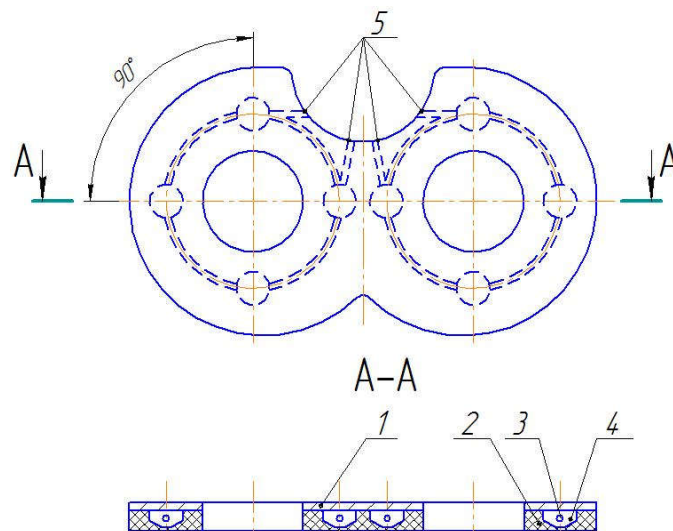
Конструкція пластини компенсації торцевого зазору: 1 - робоча поверхня; 2 - опорна поверхня; 3 - пружнодемпфуючий елемент; 4 - камери піджиму; 5 – канали для подачі рідини
